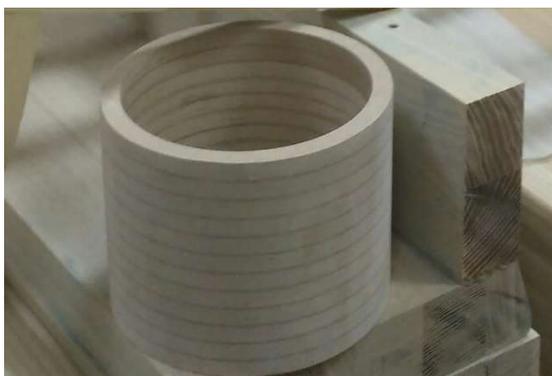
Готовый корпус рупора и цилиндрический корпус для СЧ/ВЧ динамиков
